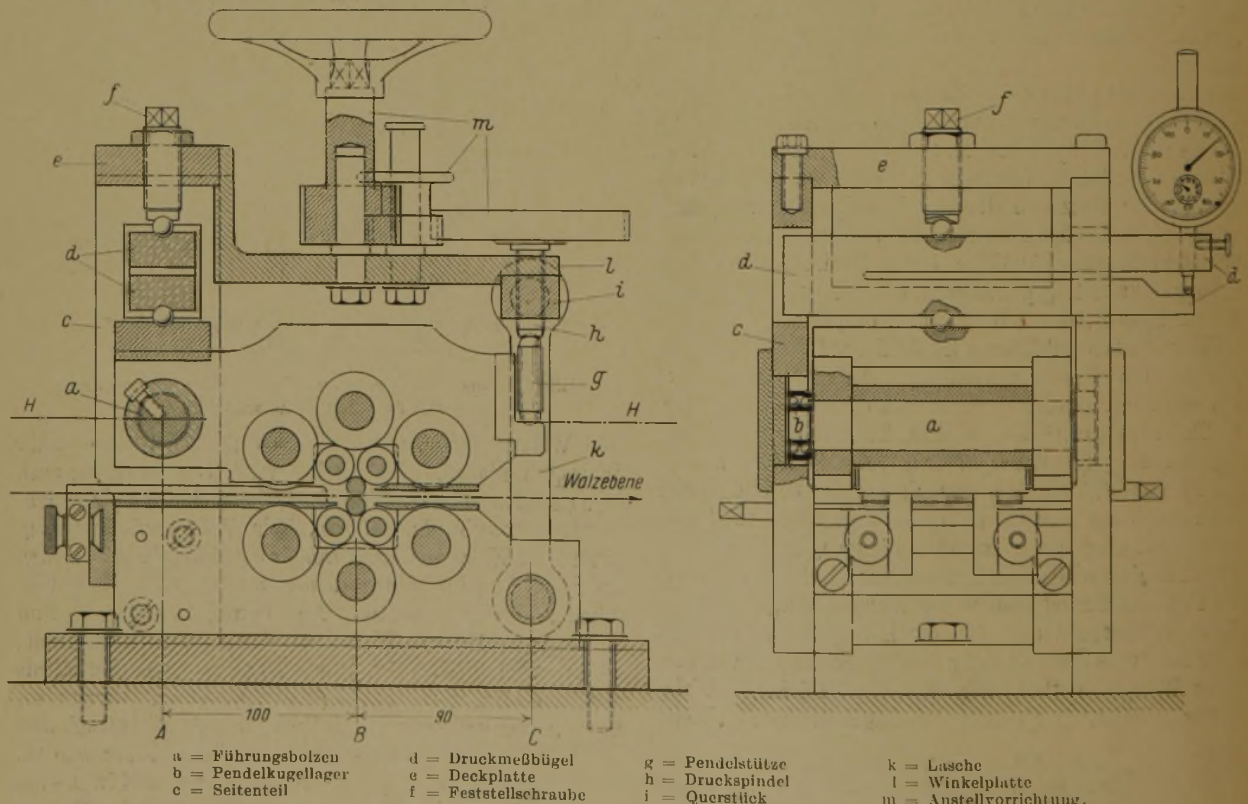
12-Walzen-Kaltwalzgerüst, Bauart Rohn.
